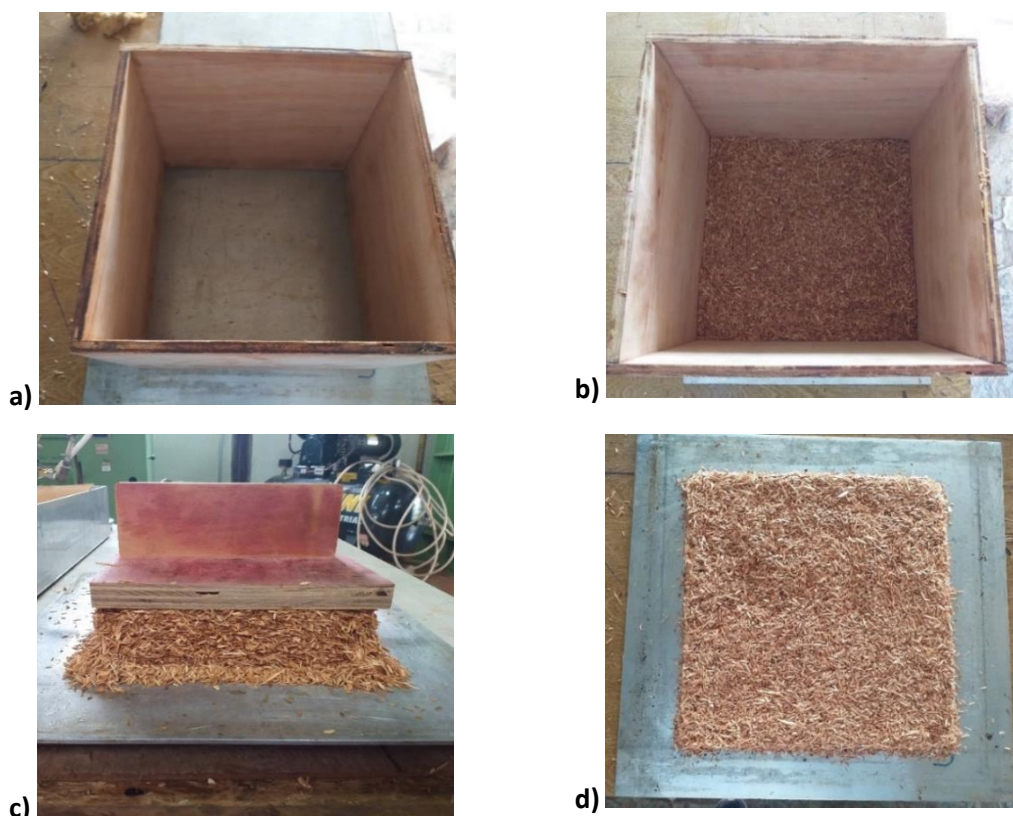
Montagem do colchão de partículas. a) Caixa formadora sobre chapa de alumínio “untada”; b) Partículas espalhadas dentro da caixa formadora; c) Tampa do molde utilizada para exercer pressão e deixar as partículas no formato do molde; d) Colchão formado. Fonte: a autora.
